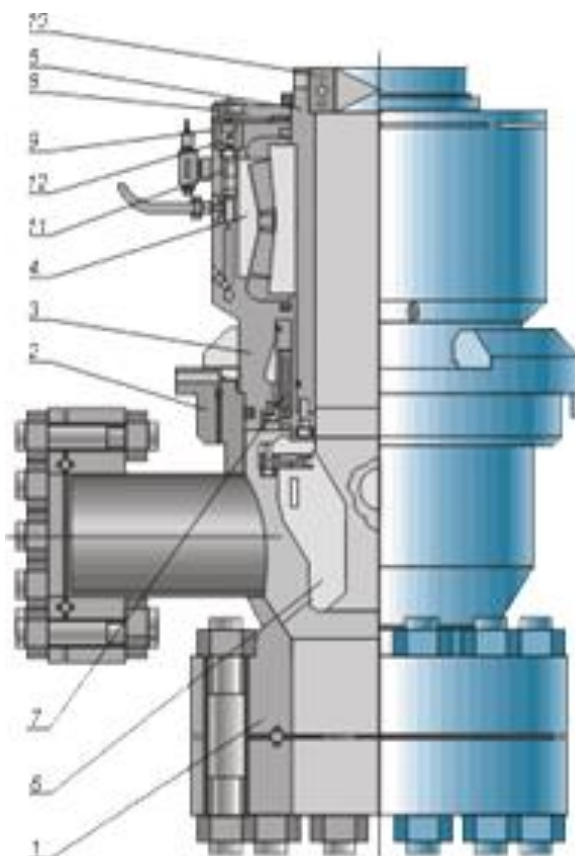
Превентор устьевой вращающийся: 1 - корпус, 2 - гайка байонетная, 3 - корпус, 4 - роликподшипник, 5 - ствол, 6 - элемент уплотнительный, 7 - уплотнение шевронное, 8 - крышка, 9 - фланец, 10 - вкладыш, 11 - насос, 12 – привод
